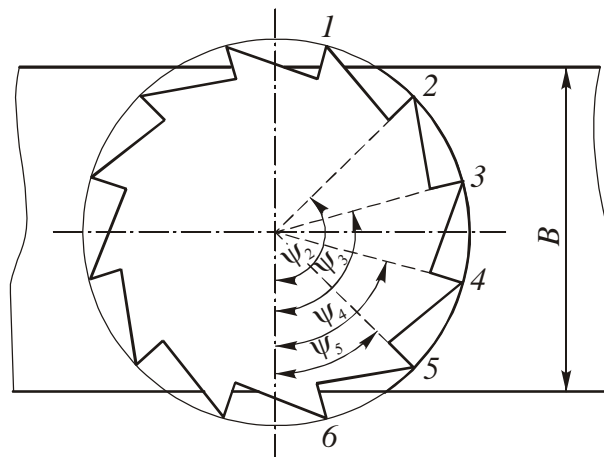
Положение зубьев торцовой фрезы на поверхности цилиндра при лобовом симметричном фрезеровании
